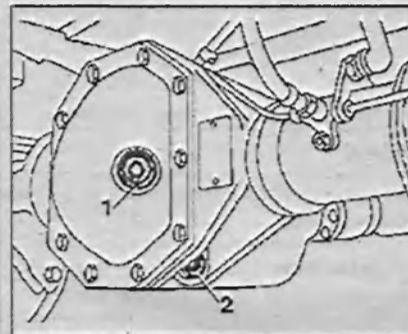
а. Задний редуктор 741.13 (HL 0):
